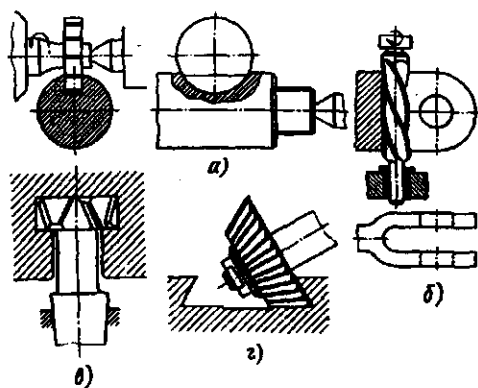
Схемы фрезерования: а - паза под сегментную шпонку; б - проушины концевой фрезой; в - Т-образного паза грибовидной фрезой; з - паза типа ласточкина хвоста угловой фрезой
